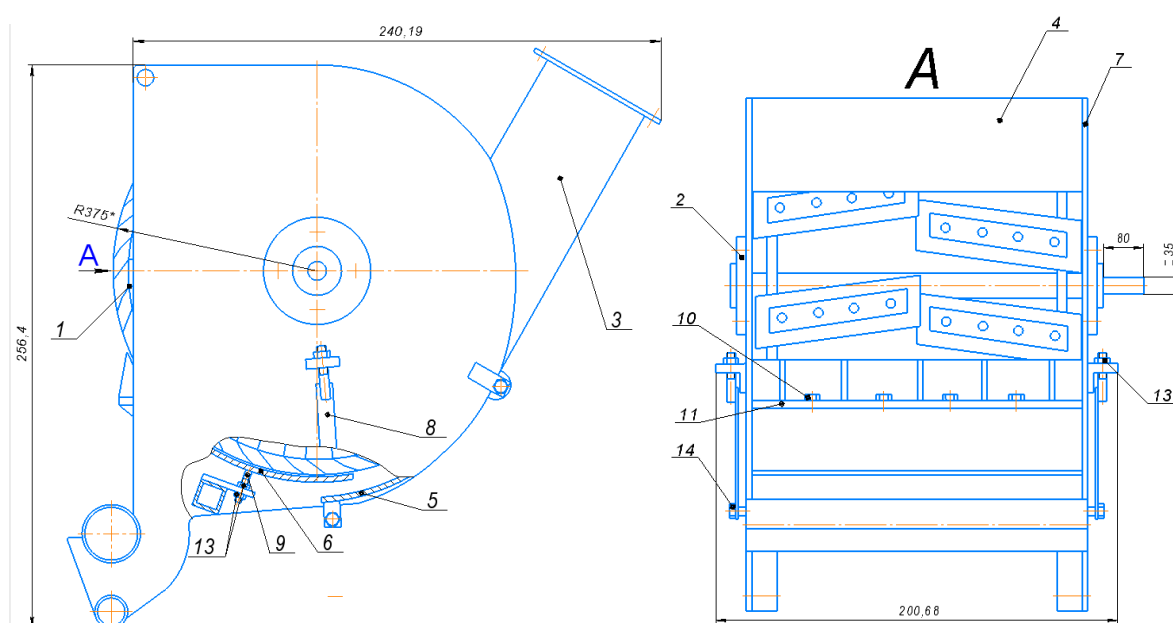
Измельчающий аппарат: 1 – барабан; 2 – вал; 3 – кожух; 4 – корпус; 5 – нижняя поверхность поддона; 6 – верхняя поверхность поддона; 7 – боковая стенка корпуса; 8 – крепежный элемент; 9 – шпилька; 10 – крепежная пластина; 11 – противорежущая пластина; 12 – уголок; 13 – ось
